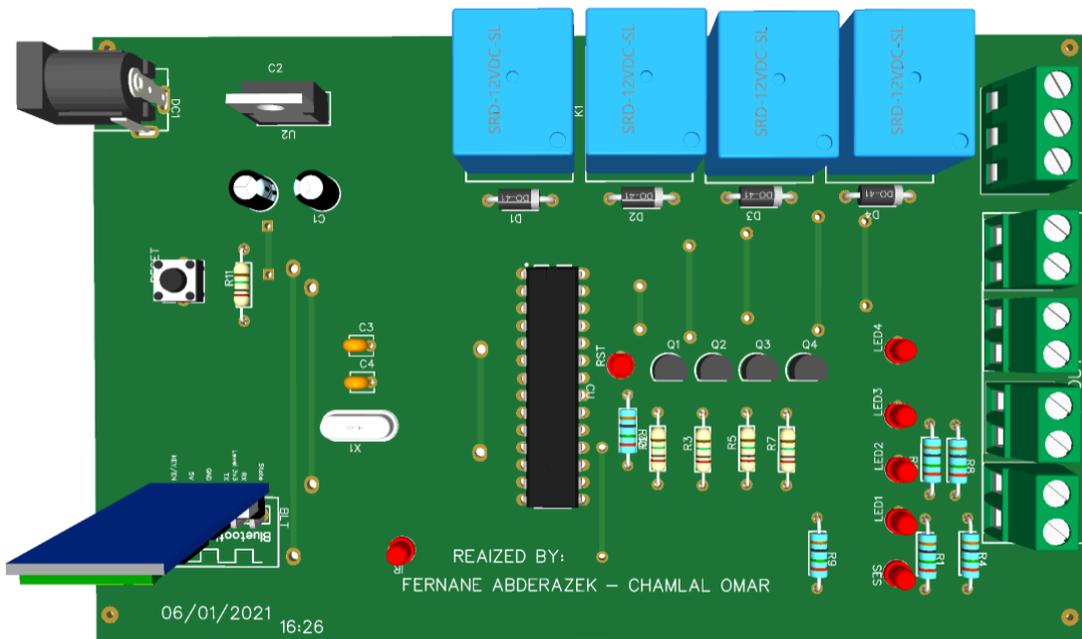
Carte PCB en 2 Dimensions avec composant Visible
